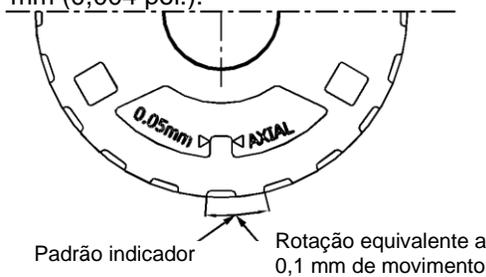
Rotação do suporte do mancal para definir a folga do rotor
